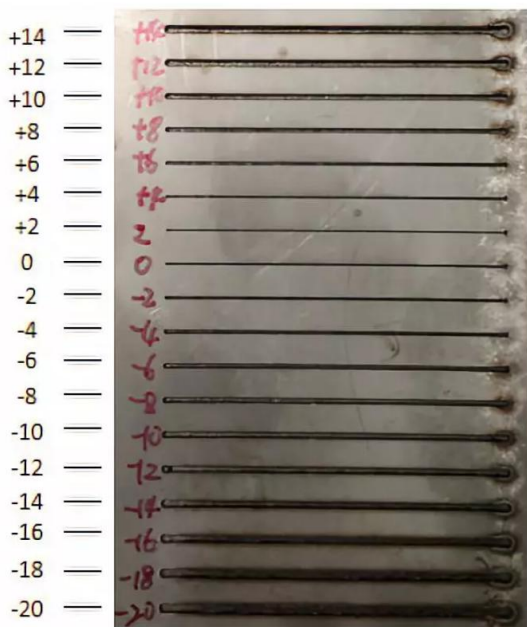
Поверхность заготовки при различных значениях фокуса
